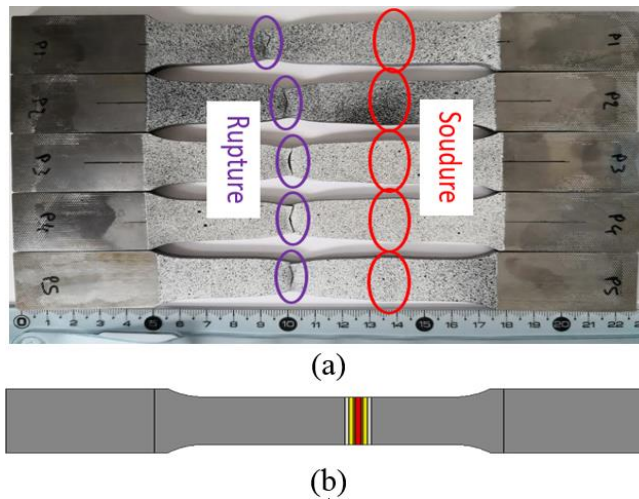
Position de la rupture et de la soudure sur cinq éprouvettes plates (a) et zones matériaux (b)
